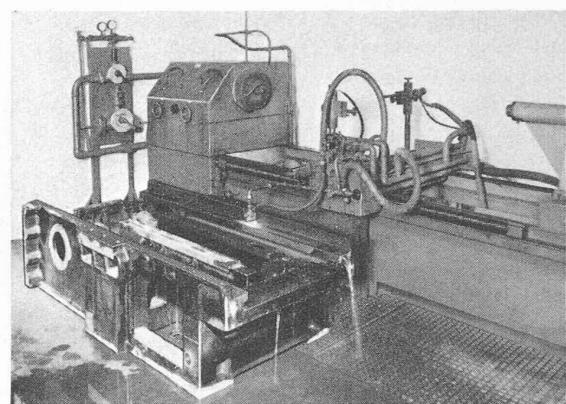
Trempe du bâti d'une presse à imprimer sur machine à tremper universelle.
